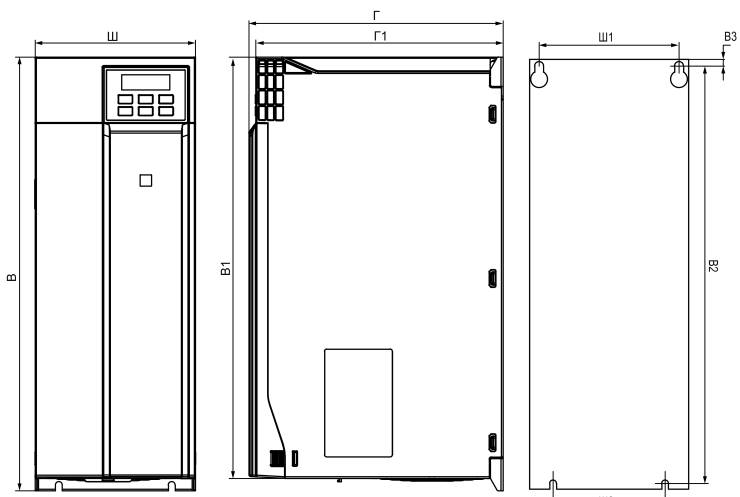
Габаритные размеры прибора в корпусе типоразмера 3
